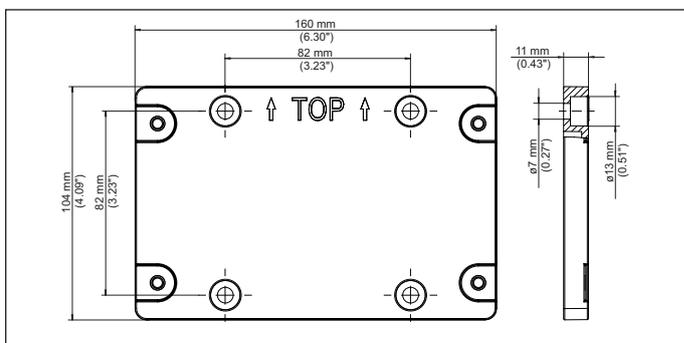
Dimensiones placa de montaje VEGAMET 841, 842
